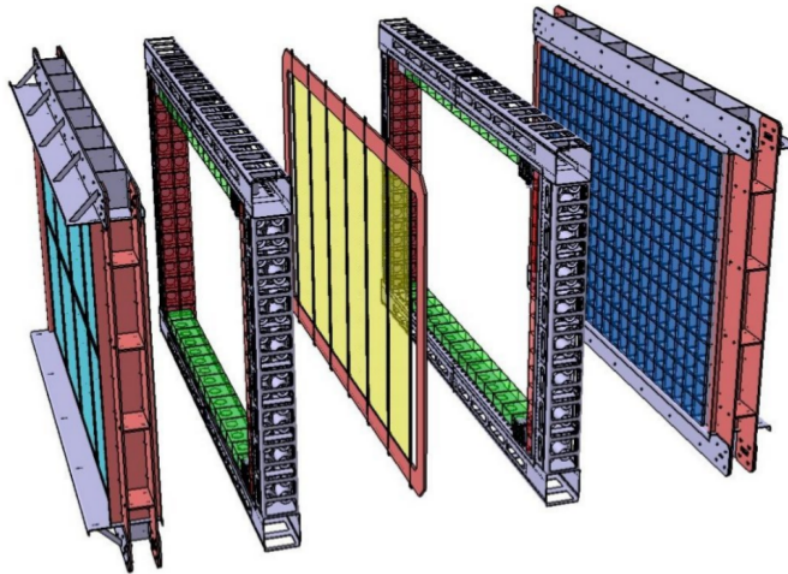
Vue éclatée du module démonstrateur de SuperNEMO.
